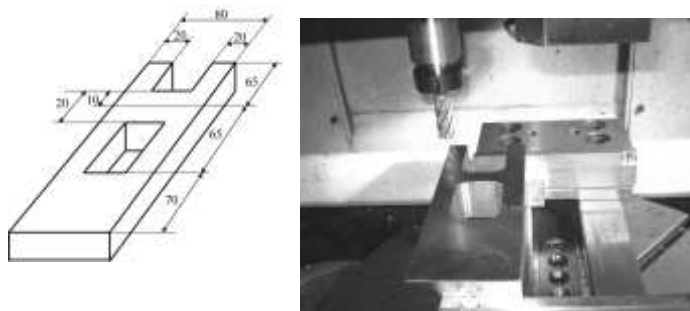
Конструкция заготовки с переменной жесткостью (слева) и наладка станка перед обработкой этой заготовки (справа)
